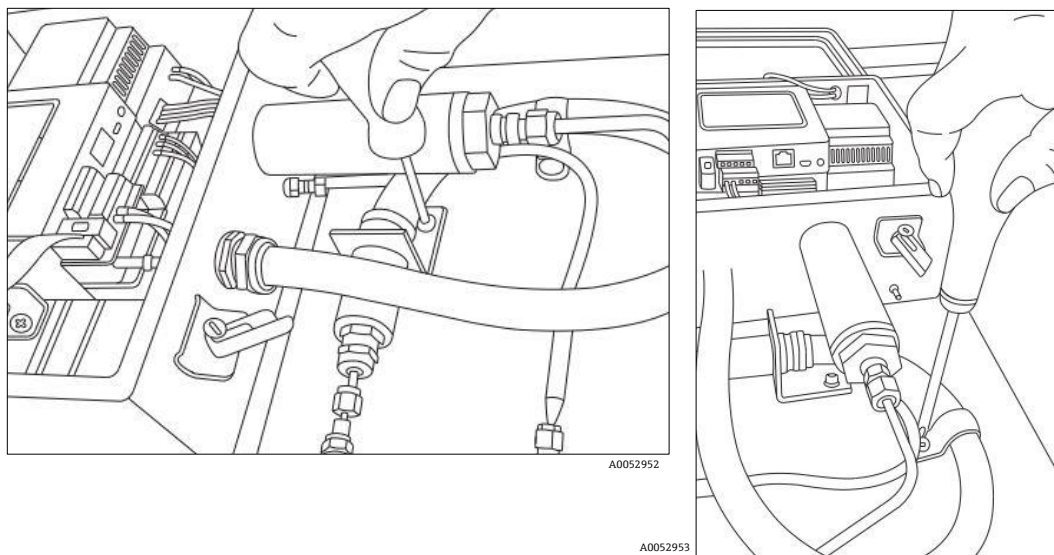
Kabelführungshalterung (links) und Klemme (rechts) entfernen
